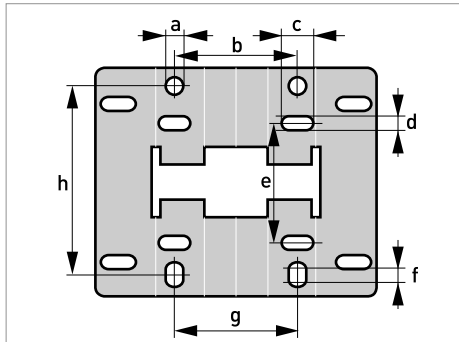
Dimensions de la plaque de montage pour boîtier mural
